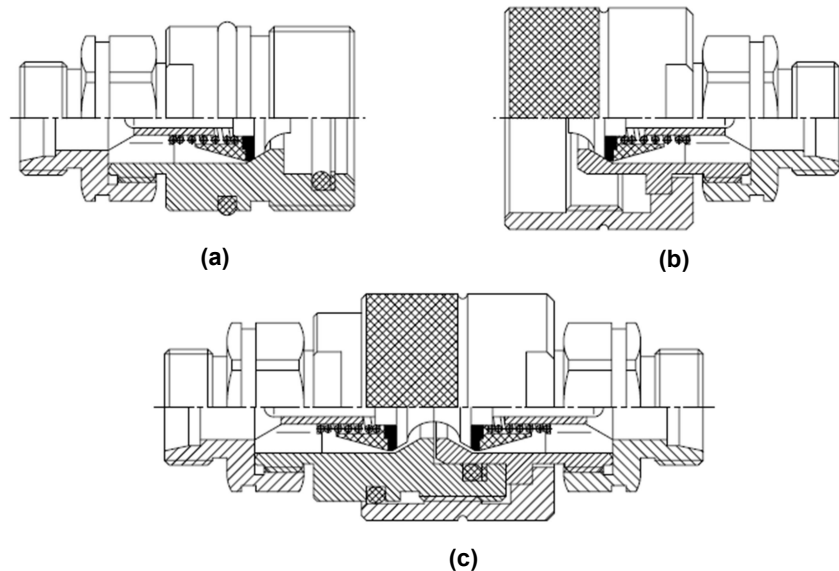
Hydraulik-Schraubkupplung mit Außengewinde⁵
